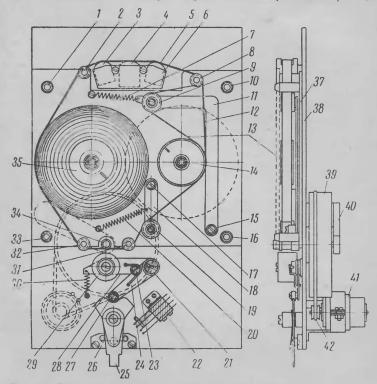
Внешний вид лентопротяжного механизма портативного диктофона с ведущим пассиком.
